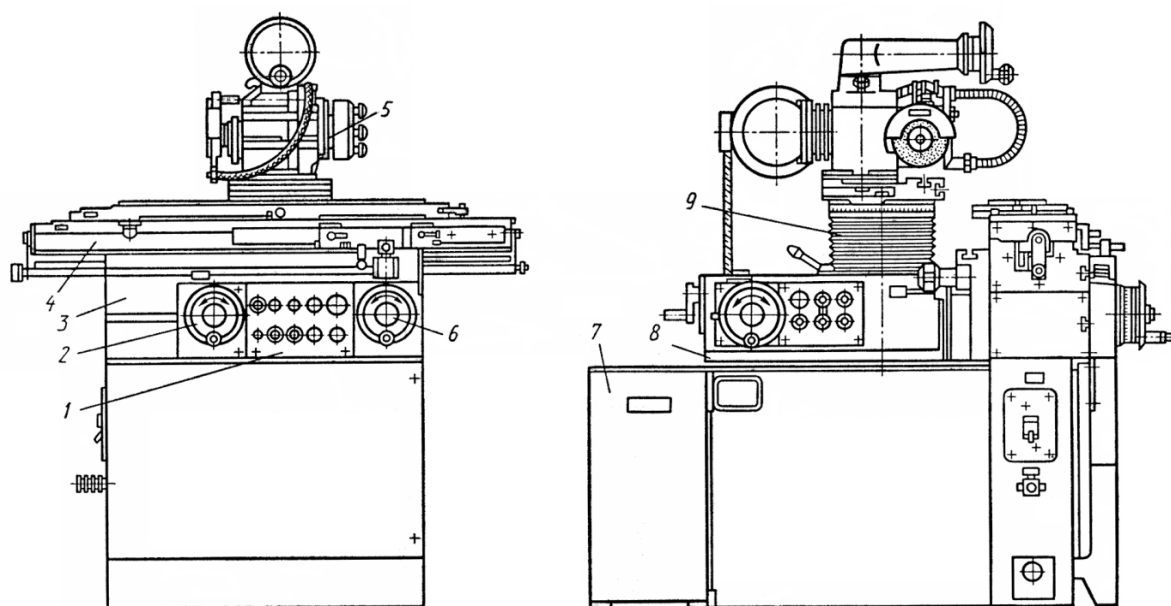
Общий вид универсально-заточного станка мод. 3М642:
